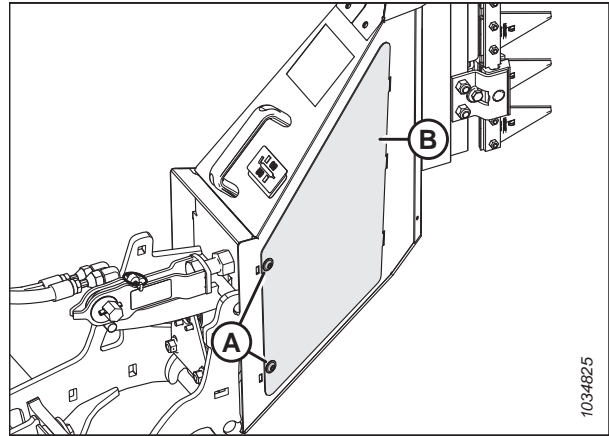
Tampa de acesso à lâmina vertical - Lado direito mostrado, lado esquerdo oposto
